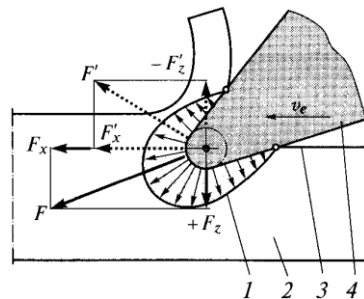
Сили, що діють від різця на заготовку: 1 – епюра тиску; 2 – заготовка; 3 – оброблена поверхня; 4 – різець
